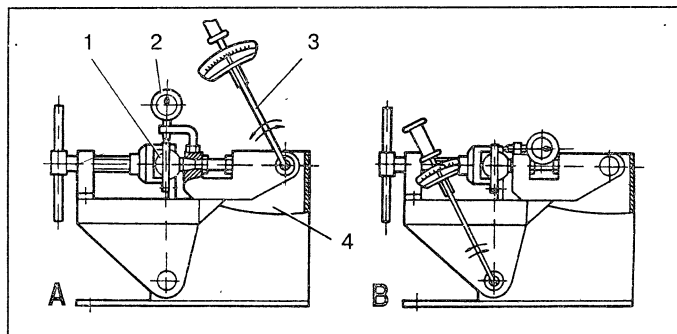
Проверка шарового шарнира на приспособлении 02.8701.9502: 1 – шаровой шарнир; 2 – индикатор; 3 – динамометрический ключ; 4 – приспособление 02.8701.9502; А – схема проверки радиального зазора; В – схема проверки осевого зазора
